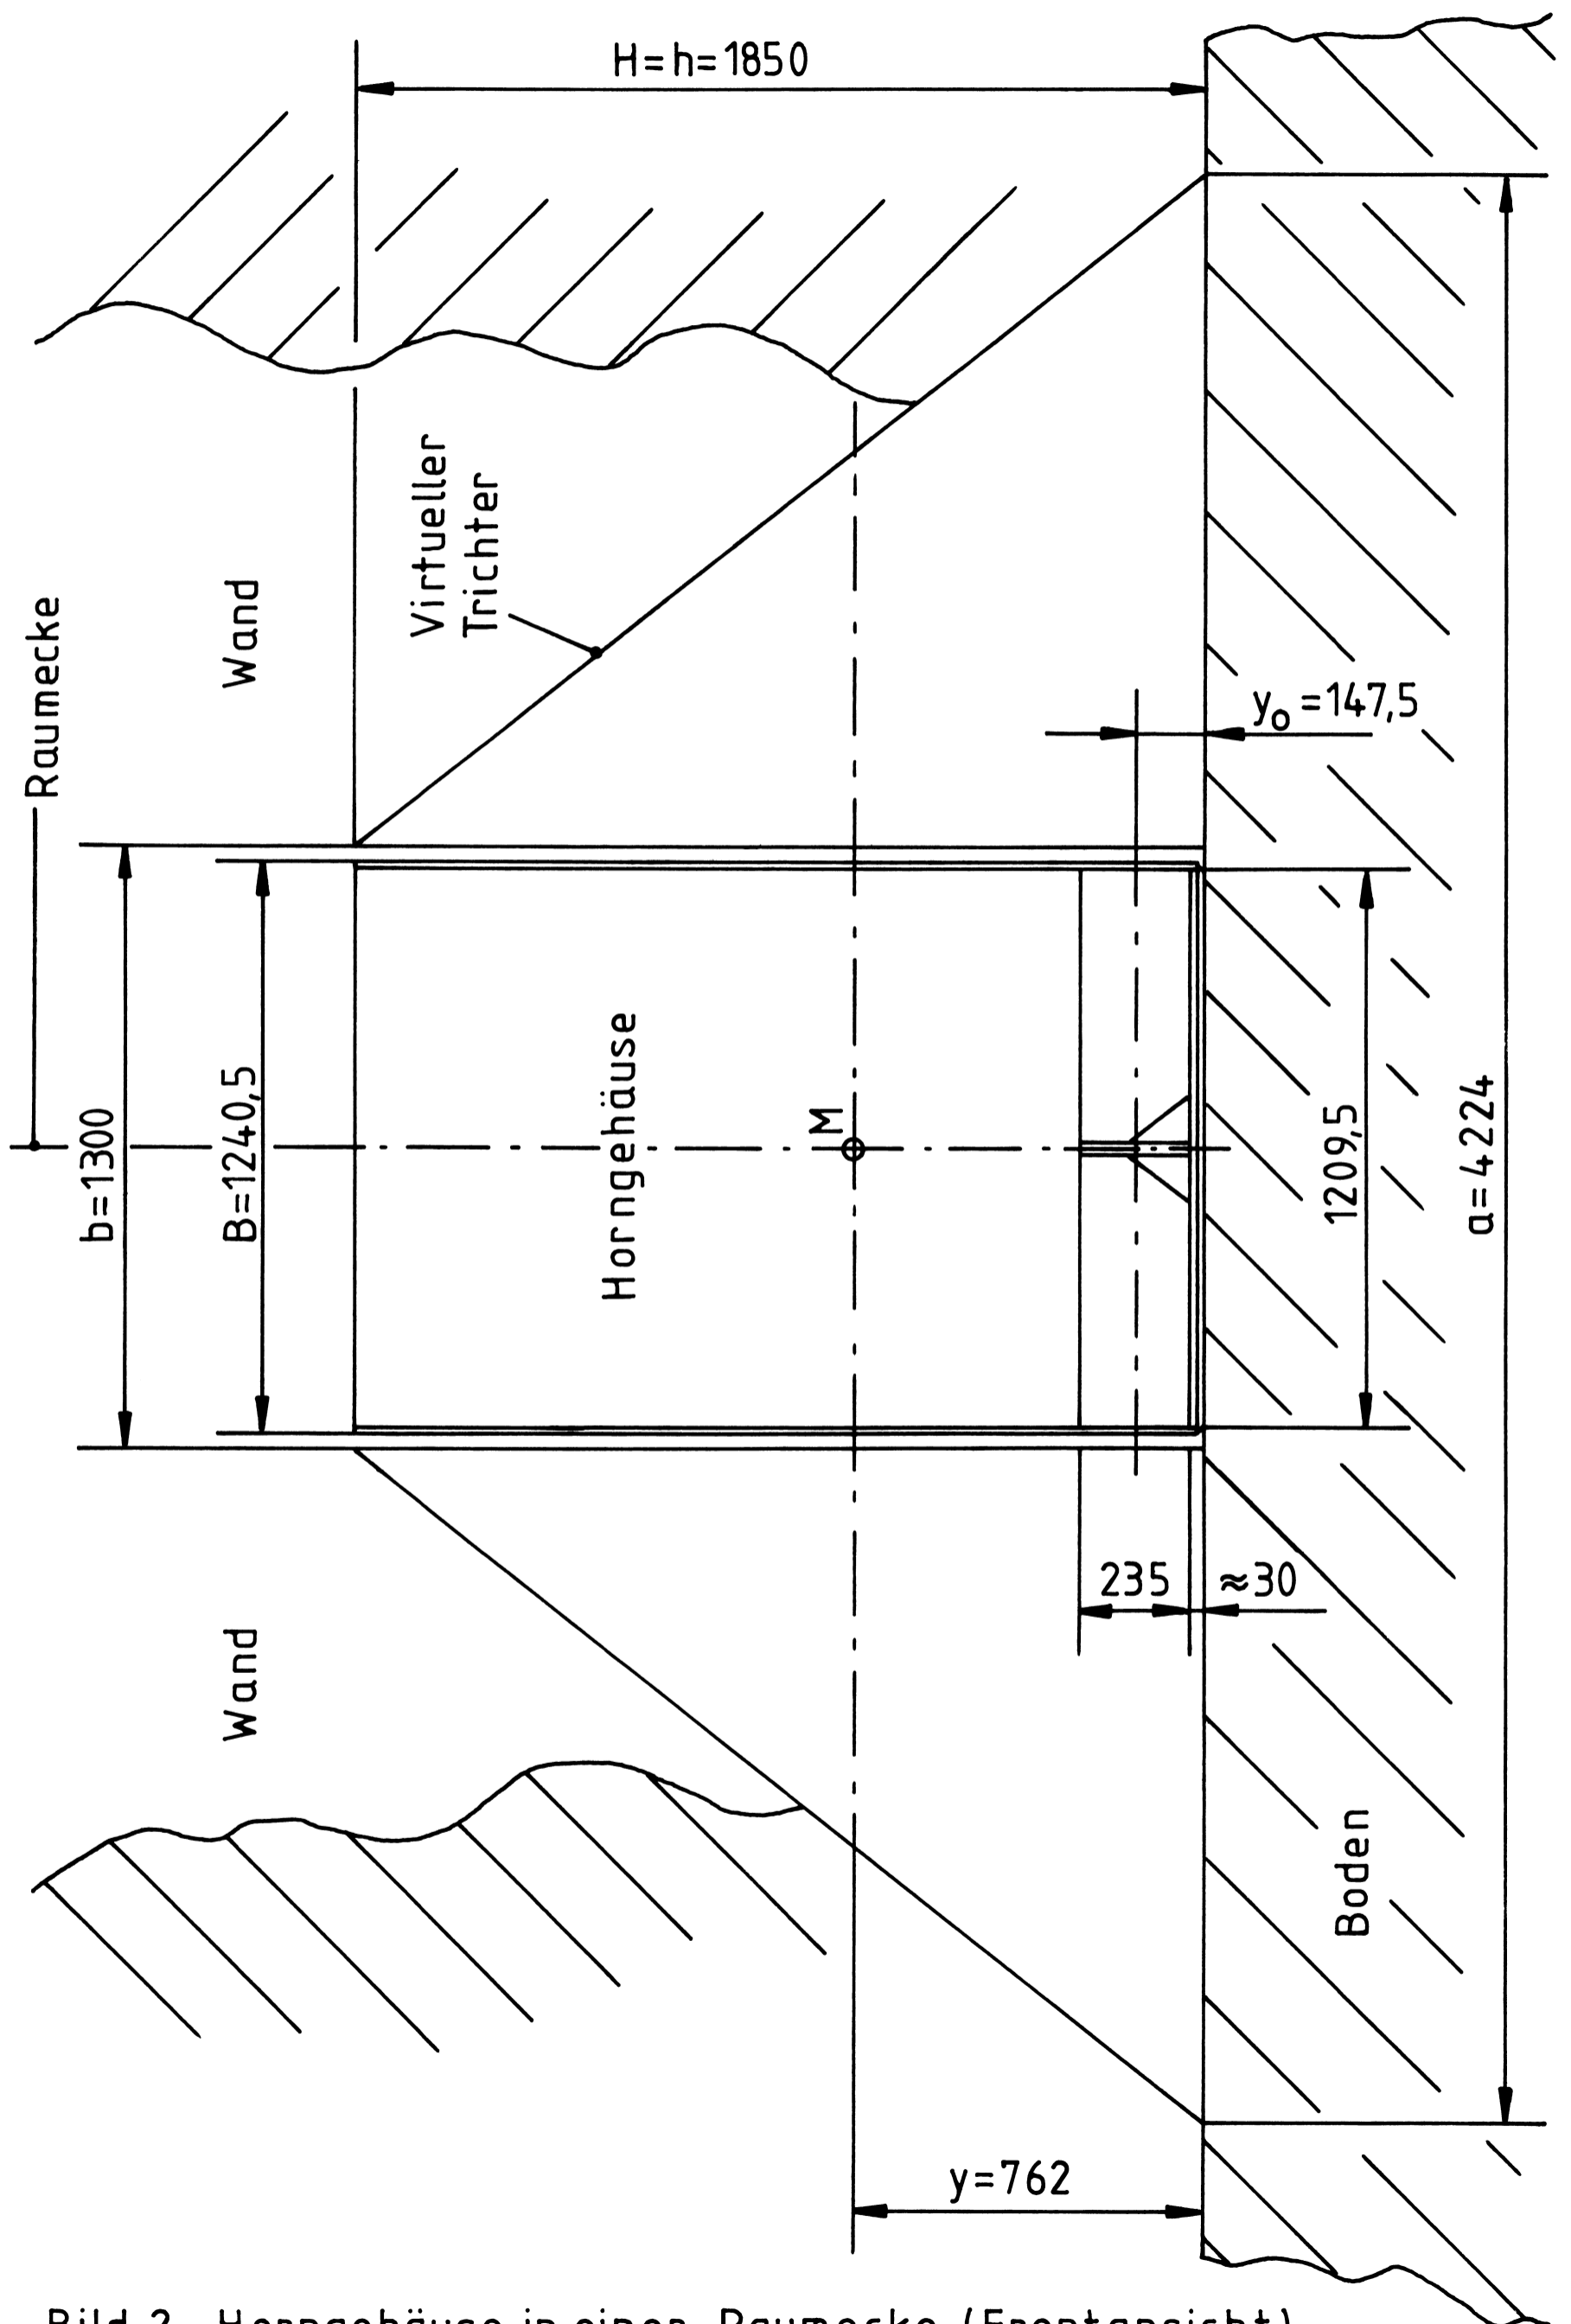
Horngehäuse in einer Raumecke (Frontansicht)
